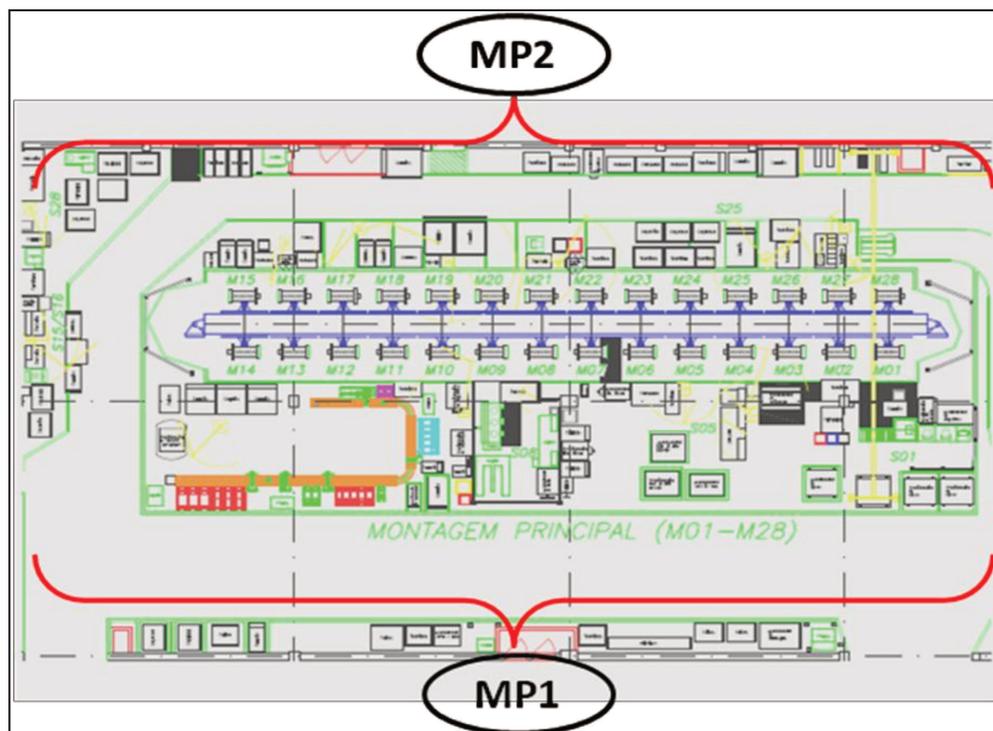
Layout do Primeiro Trecho: Primeira Parte Principal.
